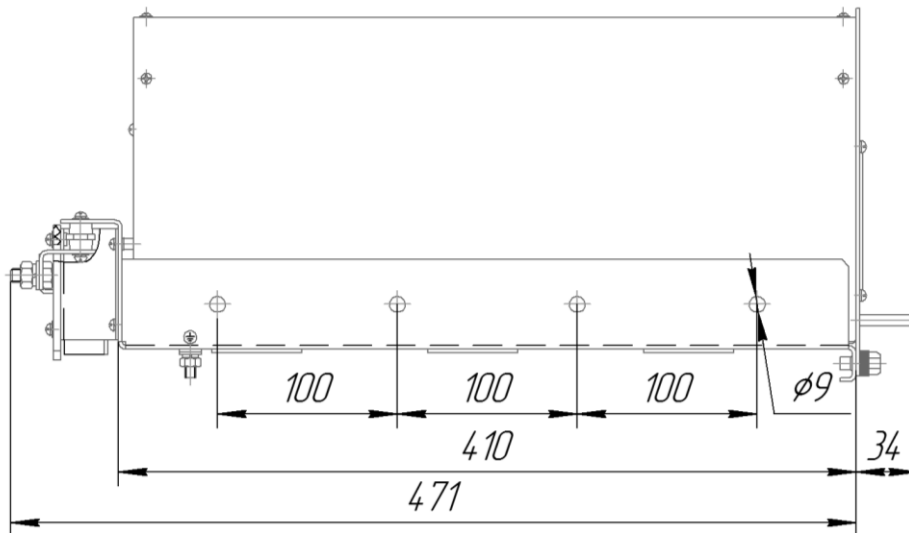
Габаритные и установочные размеры контроллера управления ЗПУ
